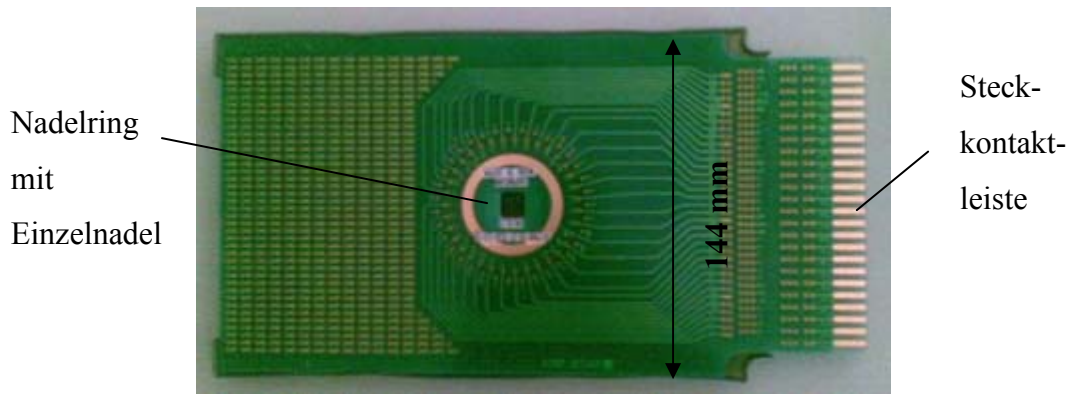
Assemblierte Einzelnadel auf PCB
